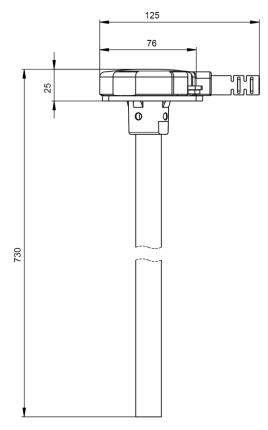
Установочные размеры. ДУТ – общий вид
